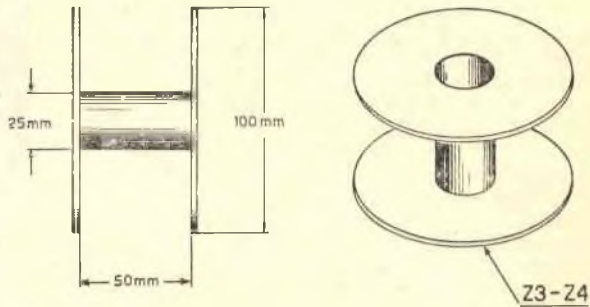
Dimensionamento del rocchetto per le impedenze Z3 e Z4
